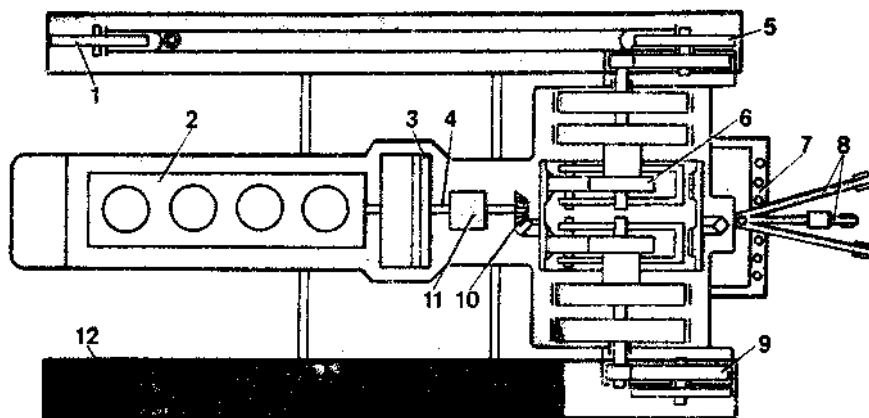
Расположение основных частей, их механизмов и деталей гусеничного трактора ДТ-75МВ:
